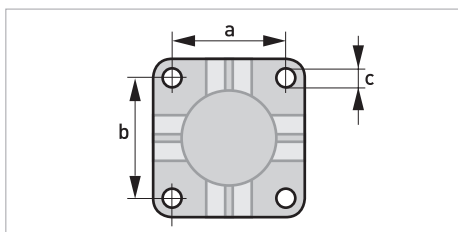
Dimensiones para placa de montaje del alojamiento de campo
